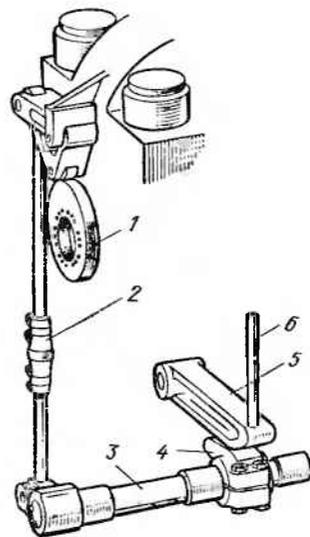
Однопозиционный привод нижнего выталкивателя:
